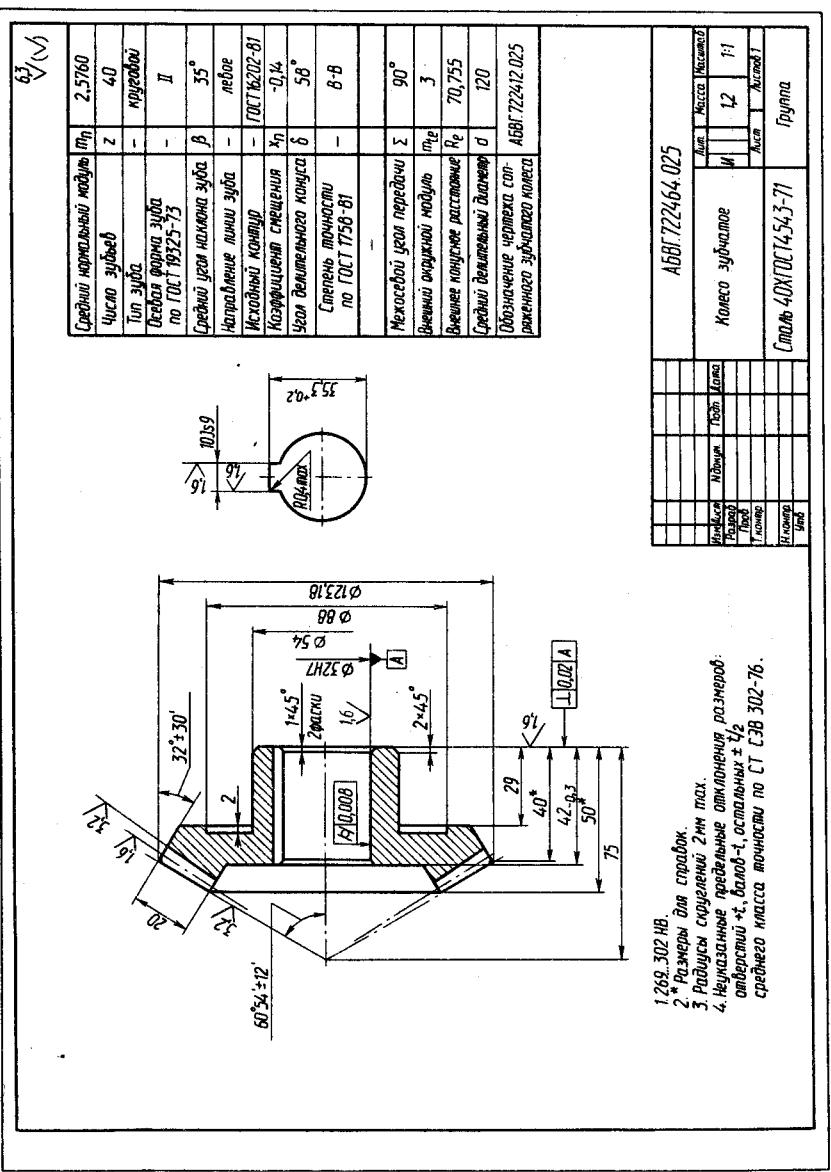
Пример рабочего чертежка коннического зубчатого колеса
